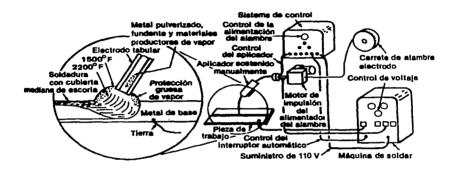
Partes componentes de un sistema para soldadura de arco metálico usando electrodo con núcleo de fundente.
